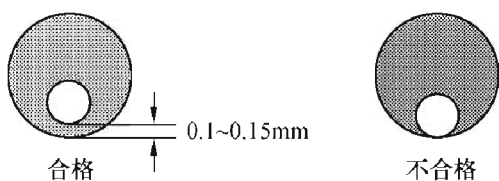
孔与焊盘中心的偏移所形成的最小环宽
